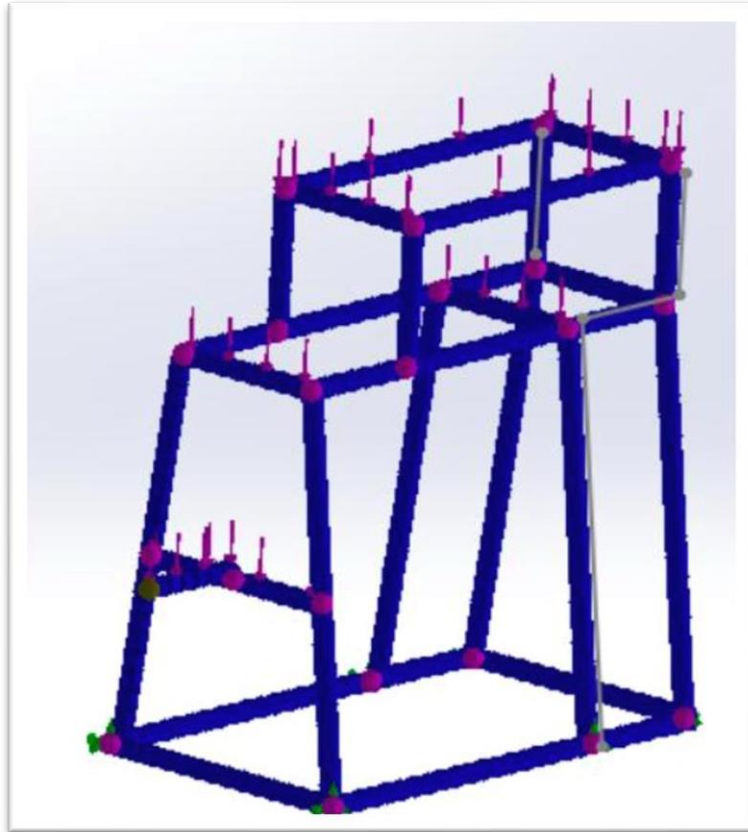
Modelado de las fuerzas aplicadas en la estructura.
